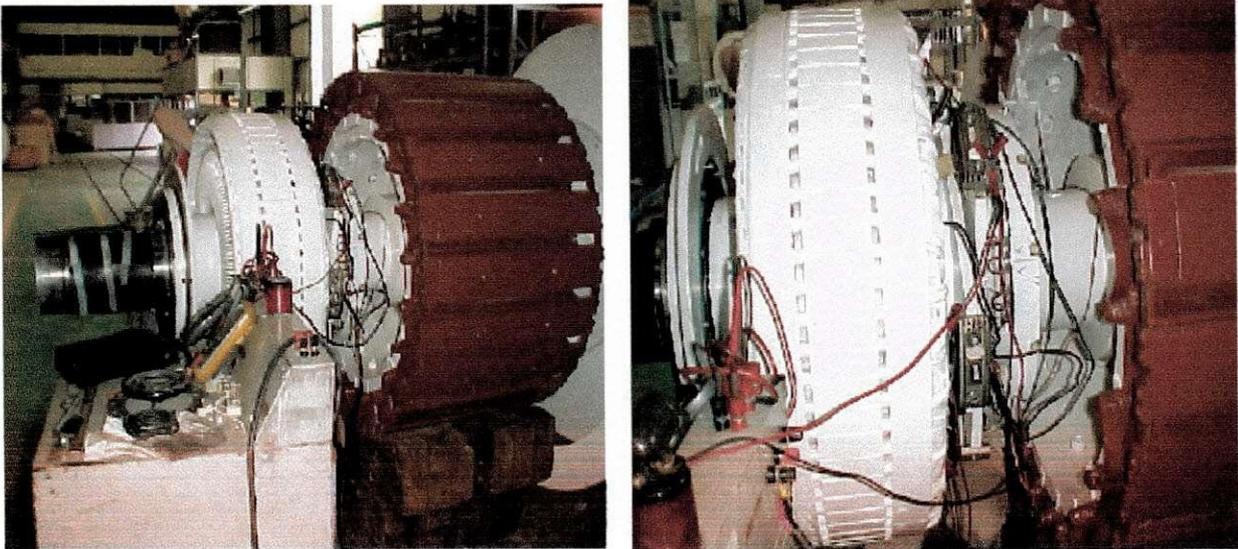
rotor, gerador interno e a roda de diodos girantes do motor síncrono sem escovas
